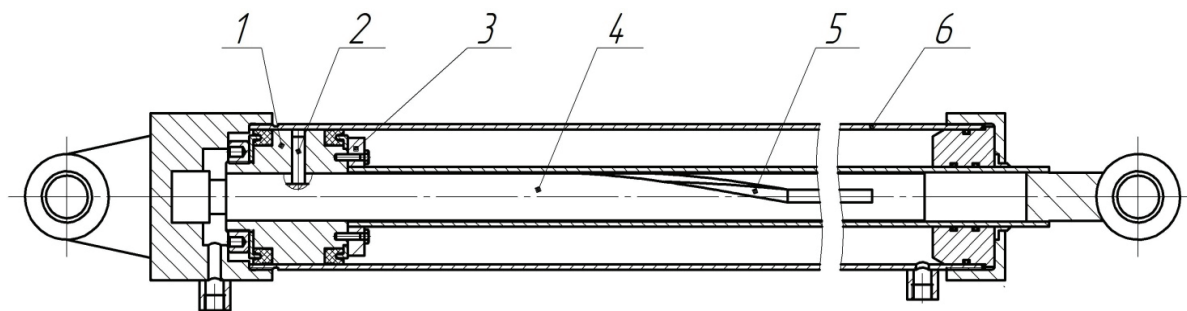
Схема гидроцилиндра перемещения выдвижной балки выносной опоры: 1 – поршень; 2 – штифт; 3 – фланец; 4 – направляющая; 5 – винтовая проточка; 6 – шток.
